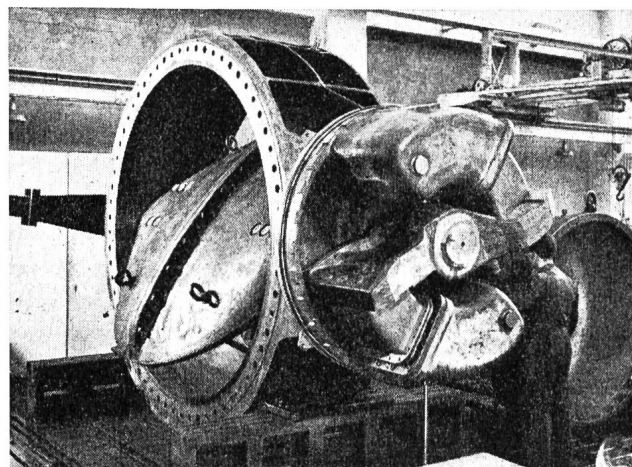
Wasserschloß Handeck II: 2700 mm Drosselklappe, 10 at, mit doppelwirkendem Ringkolbenantrieb, geöffnet (v. Roll, Klus).
